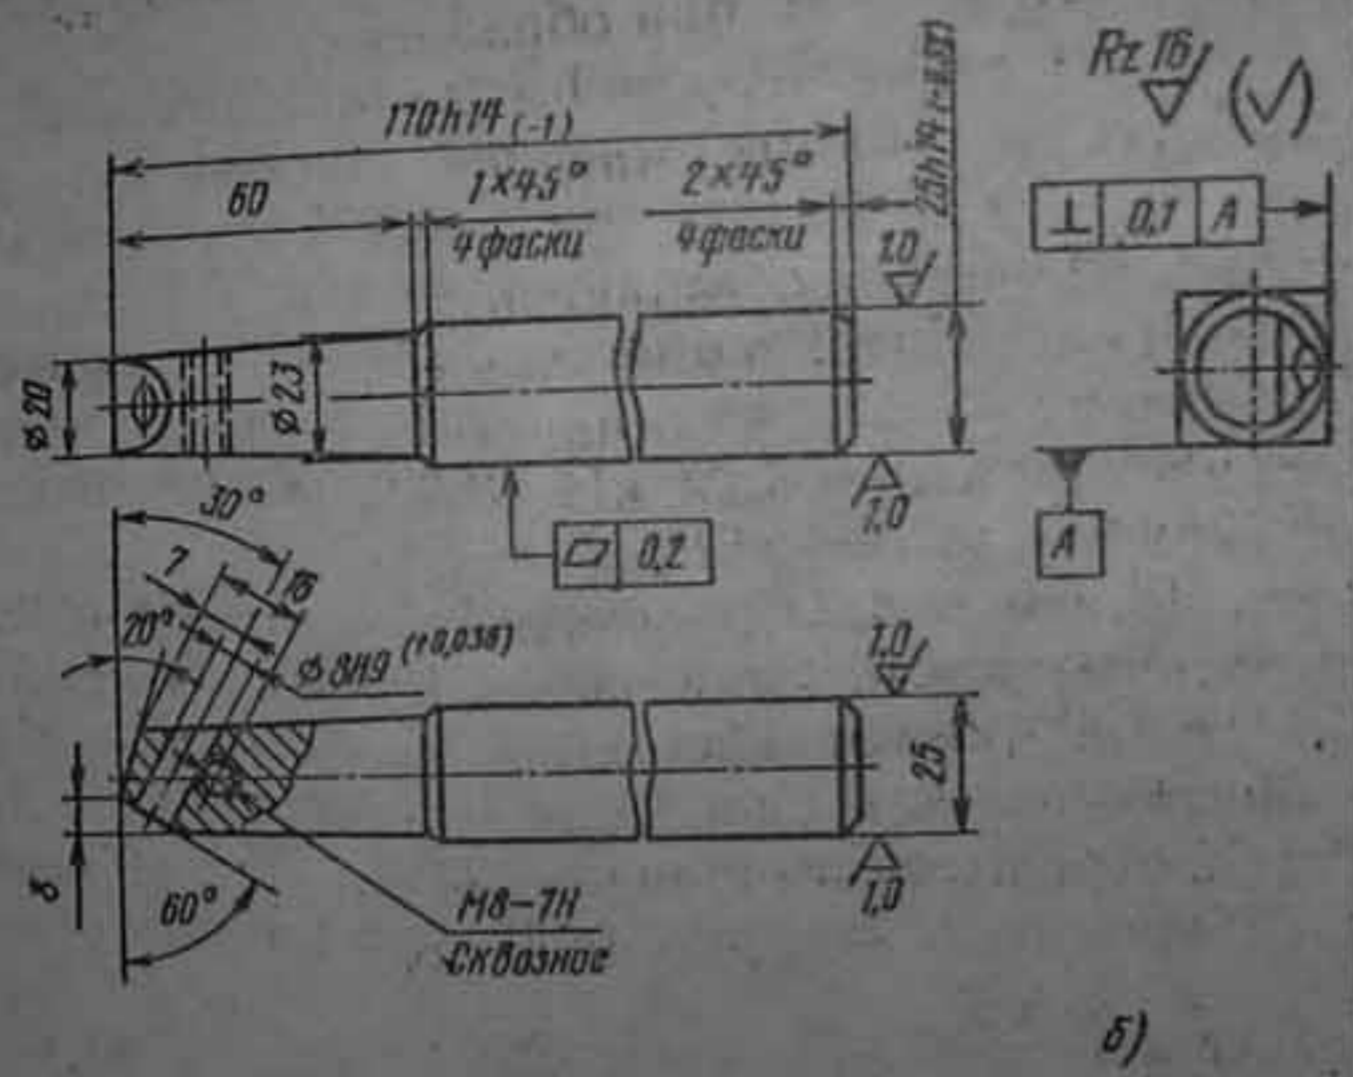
Расточной сборный резец с механическим креплением вставки из эльбором-Р:
